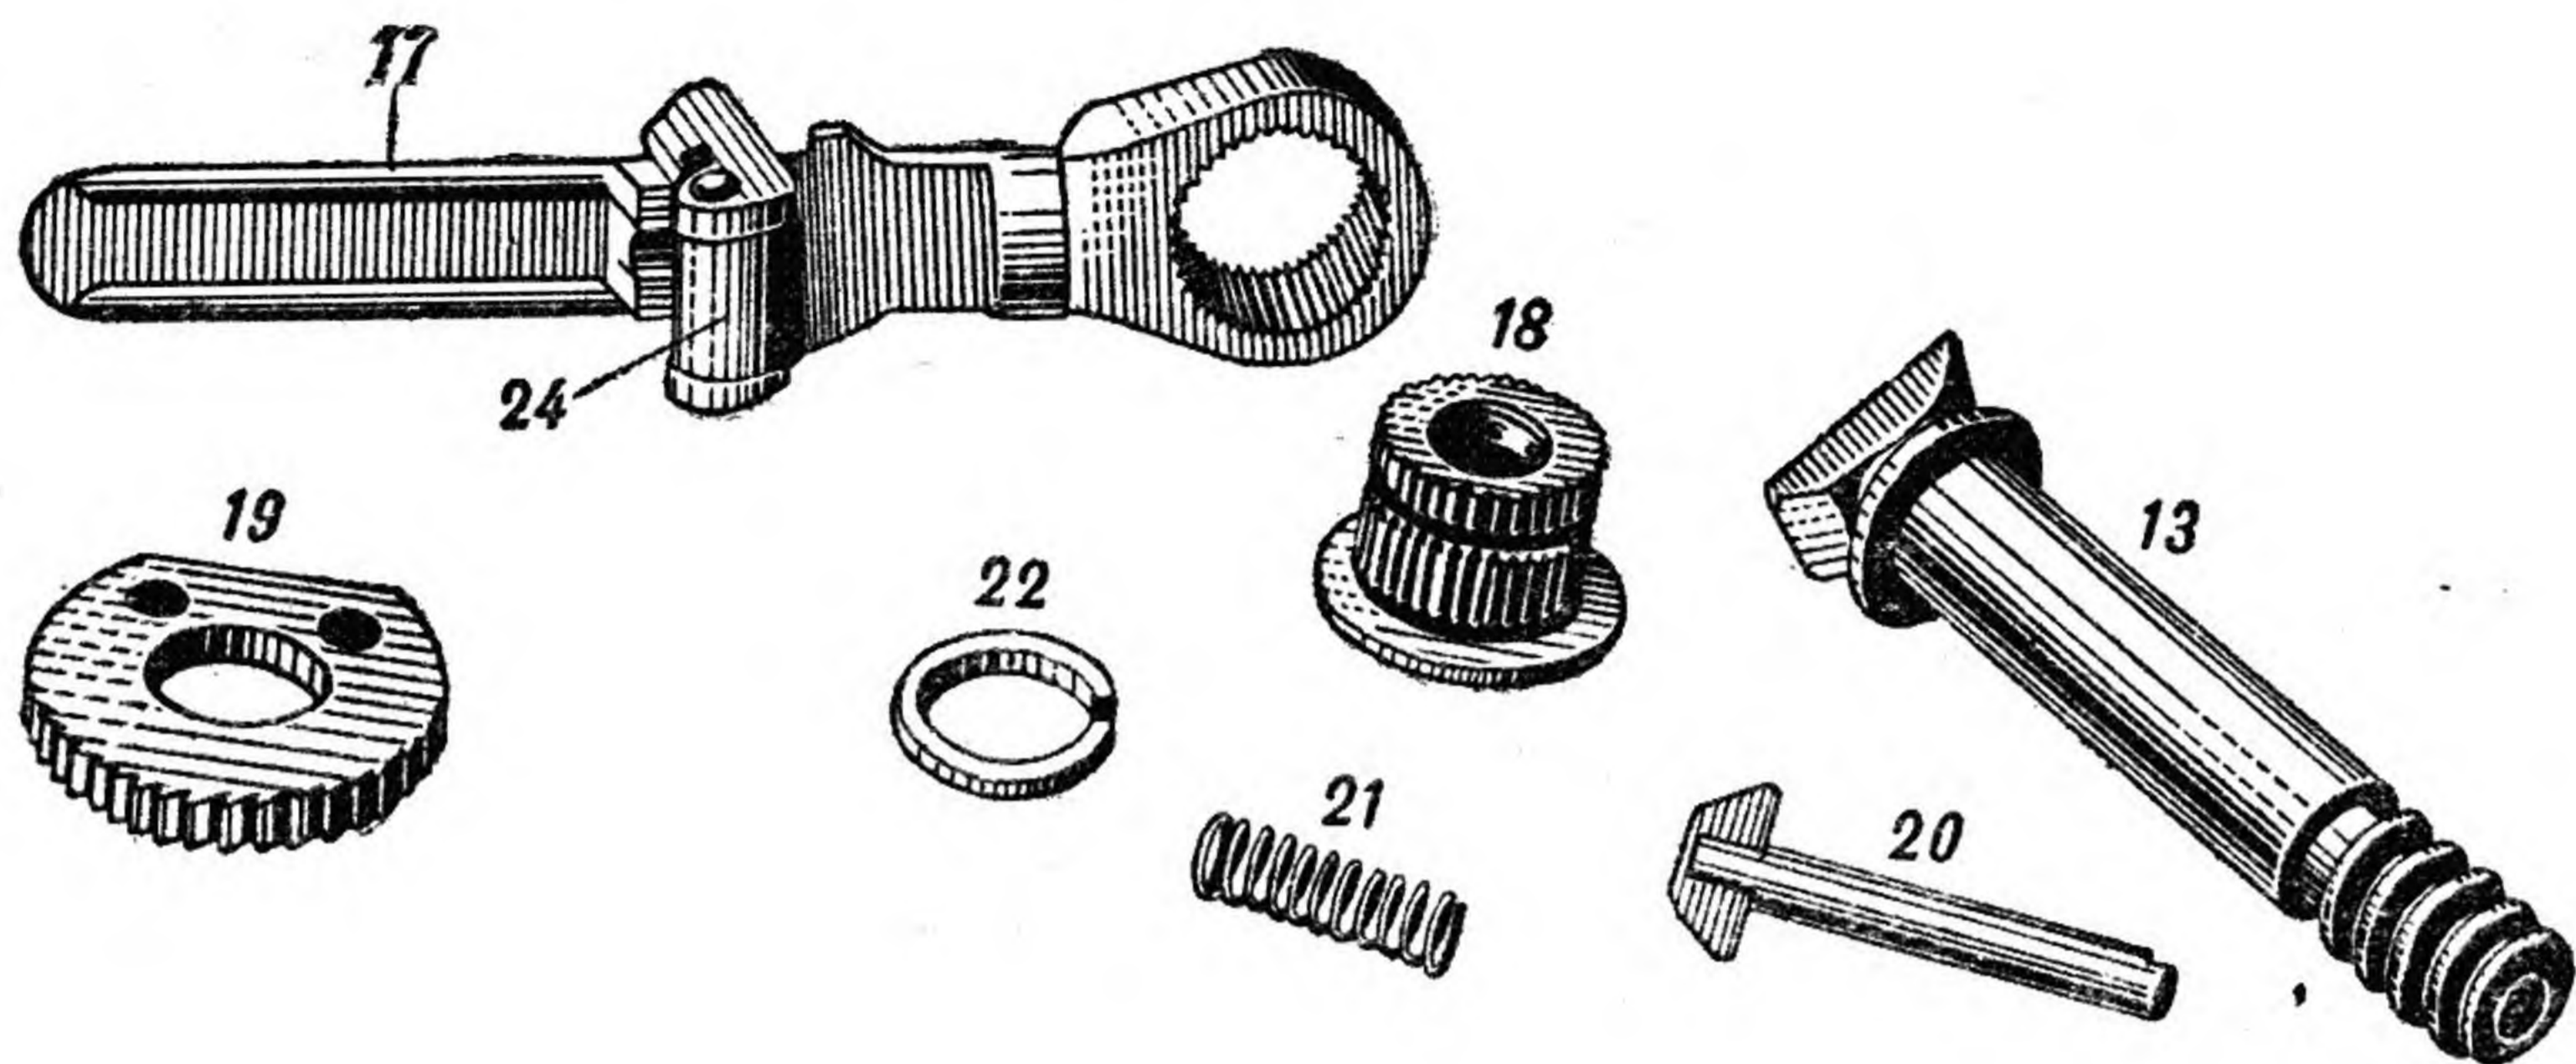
Детали стопора походного крепления верхнего станка на нижнем
